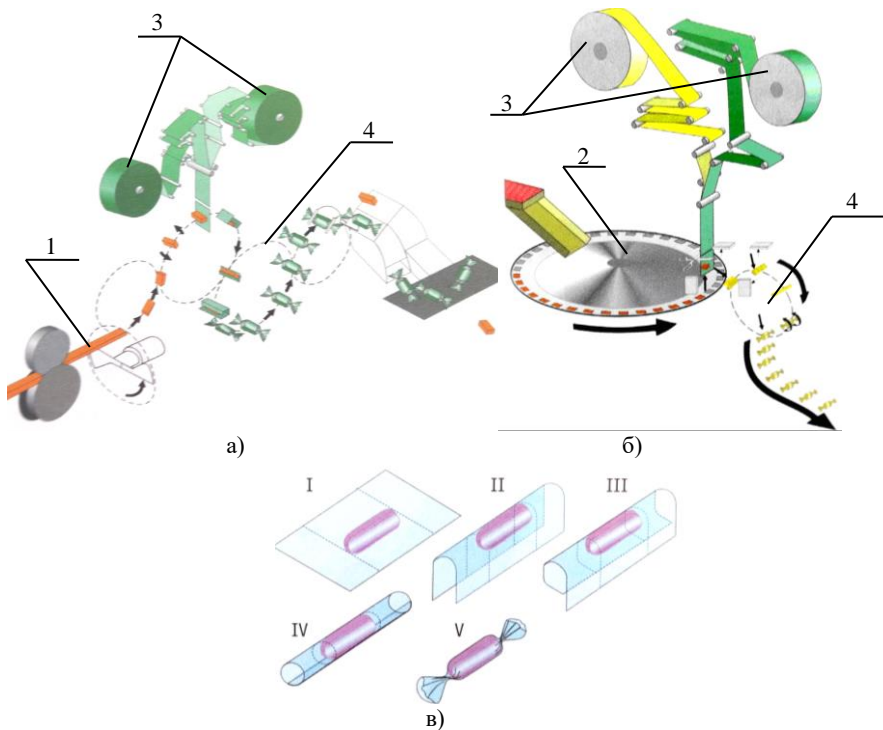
Технологія загортання цукерок “в перекрутку”: а) технологічна схема пакування з нарізанням із джгута-заготовки; б) технологічна схема пакування з поштучною подачею з живильника; в) послідовність загортання; 1 – джгут-заготовка; 2 – живильник; 3 – рулони пакувального матеріалу; 3 – загортувальний ротор.
